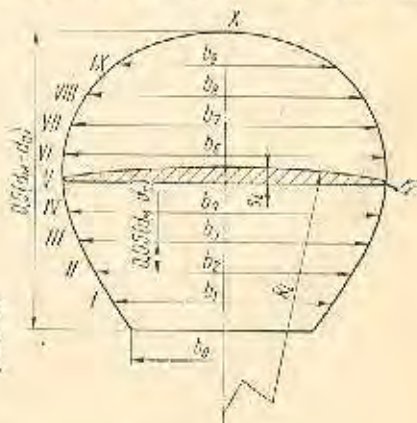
Развертка лопасти трехлопастного пропеллерного перемешивающего устройства по МН 5874—66
